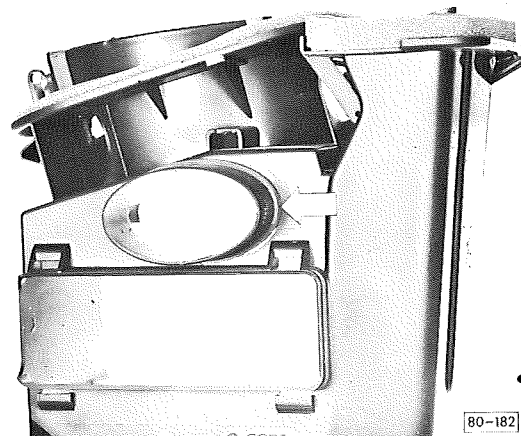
Désassemblage et assemblage du caisson d'air frais
